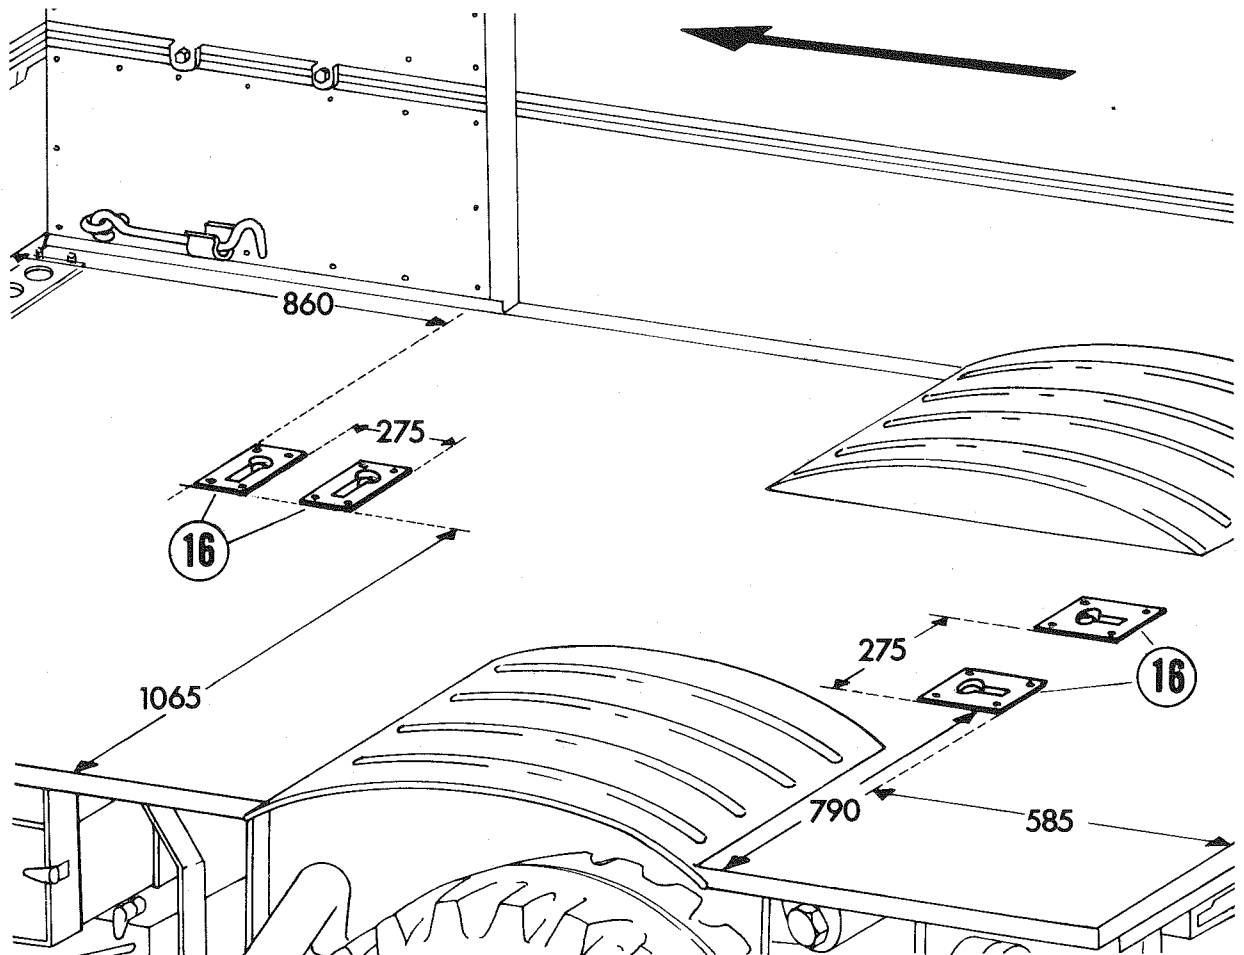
Einbaumaße für Aufnahme Stuhlbefestigung
